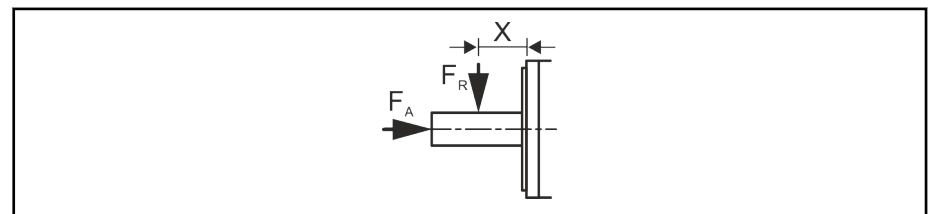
Punto de efecto de la fuerza radial F_R y la fuerza axial F_A
